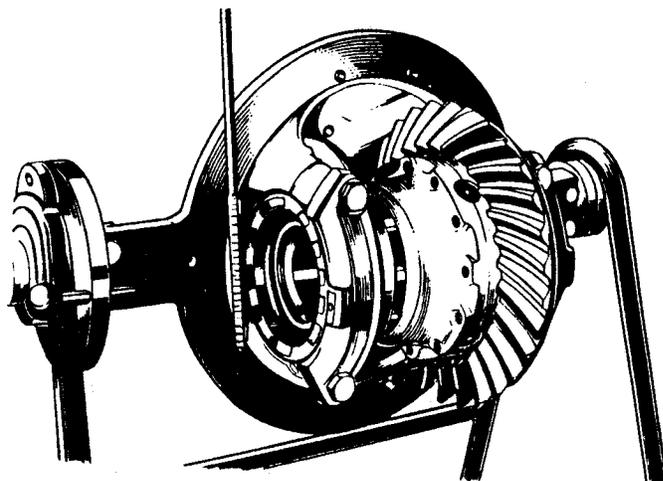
Ключ Т 17 - 393 для опорного кольца подшипника дифференциала
